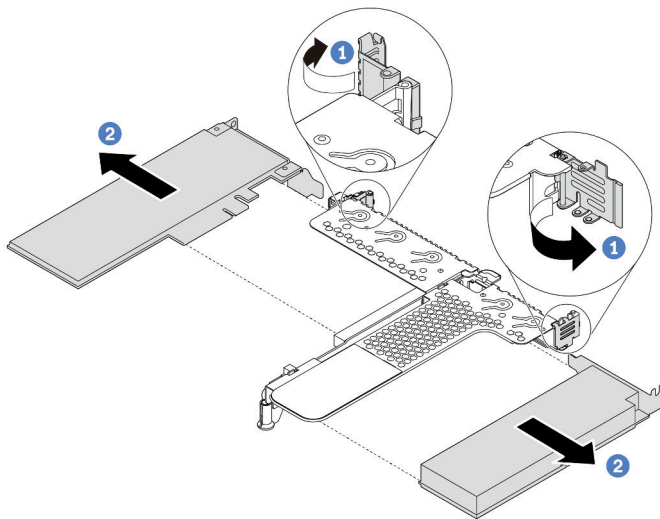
Remoção do adaptador PCIe do conjunto de placa riser LP-FH
